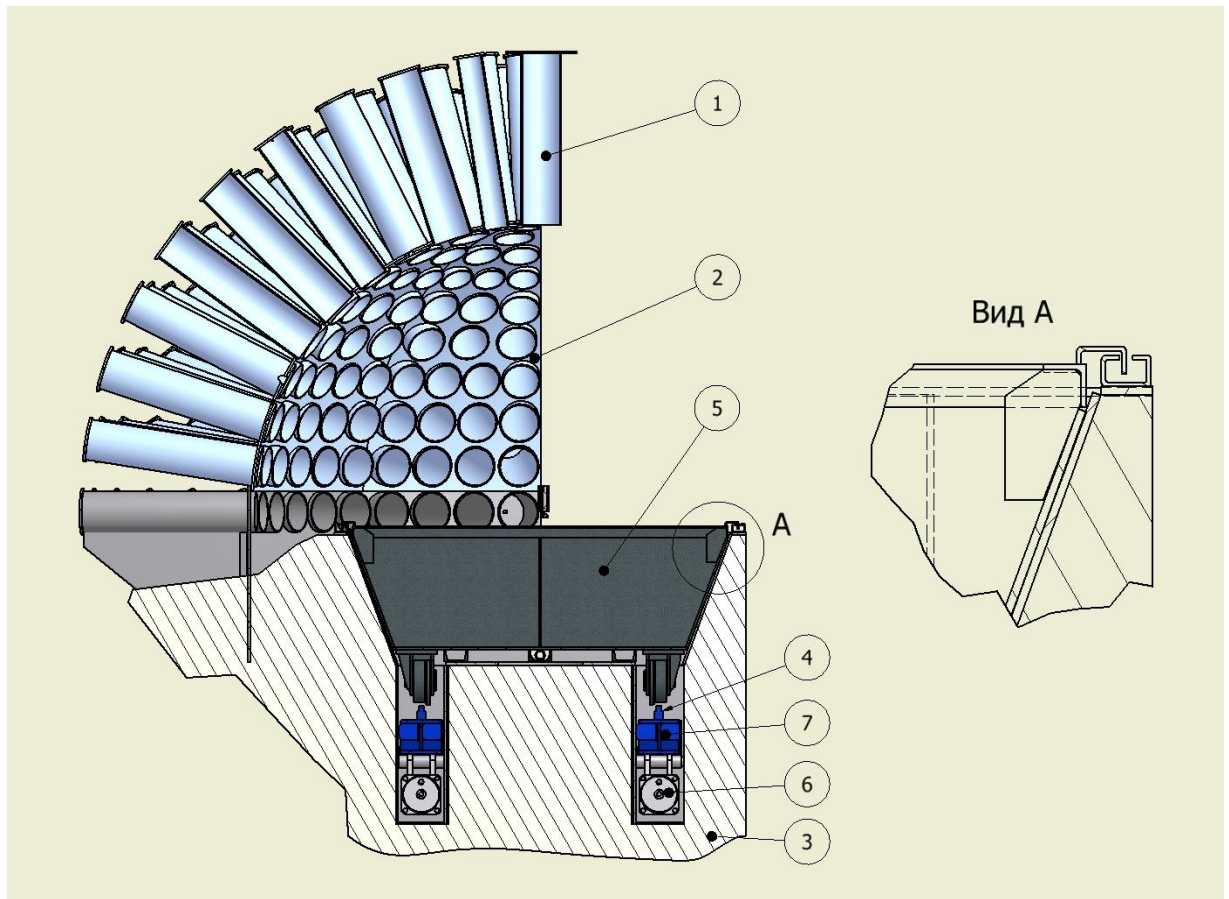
Переріз трубчастої вибухової камери 1 – труби; 2 – корпус камери; 3 – бетонна основа камери; 4 – рейковий шлях; 5 – рухомий візок; 6 – пневмоцилінри; 7 – рухомі балки;
